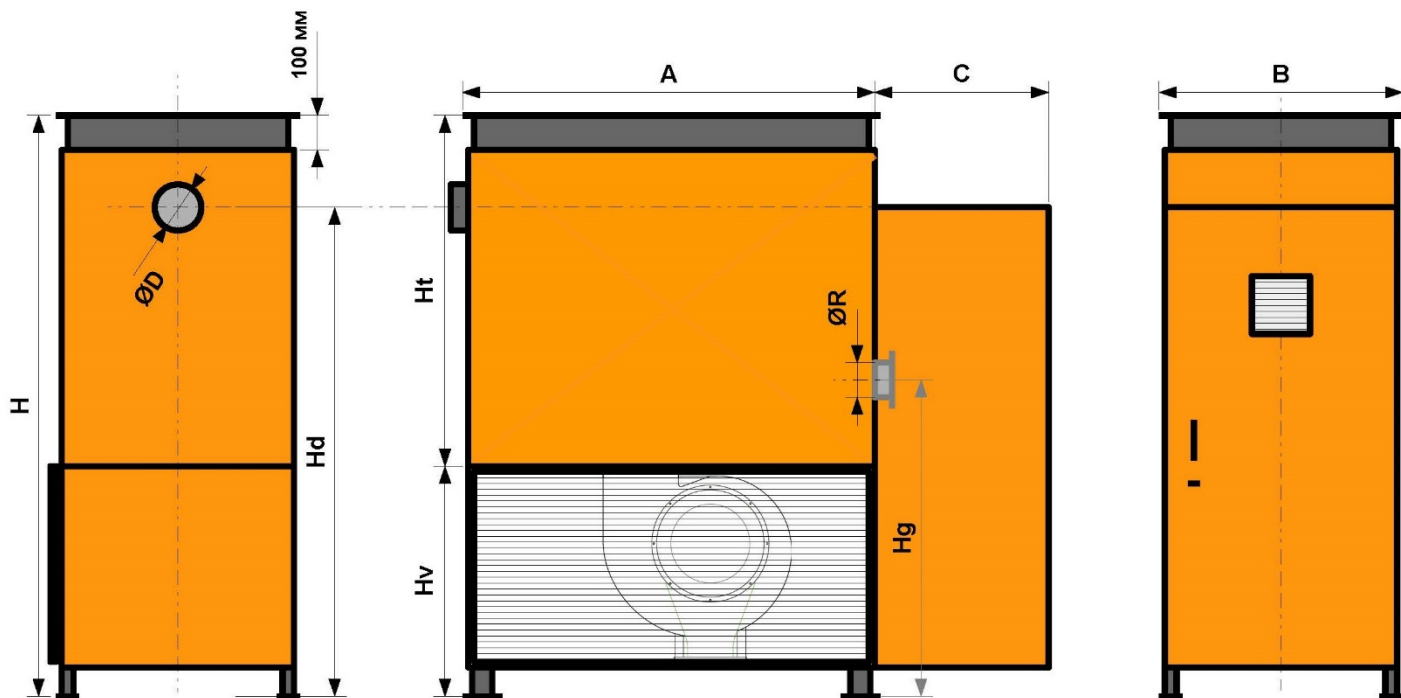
Габаритные размеры воздухонагревателей (теплообменников) серии VT-O
